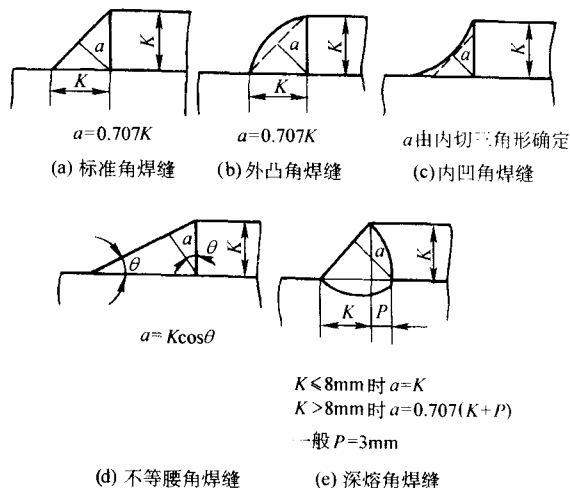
常用角焊缝的截面形状及其设计截面
